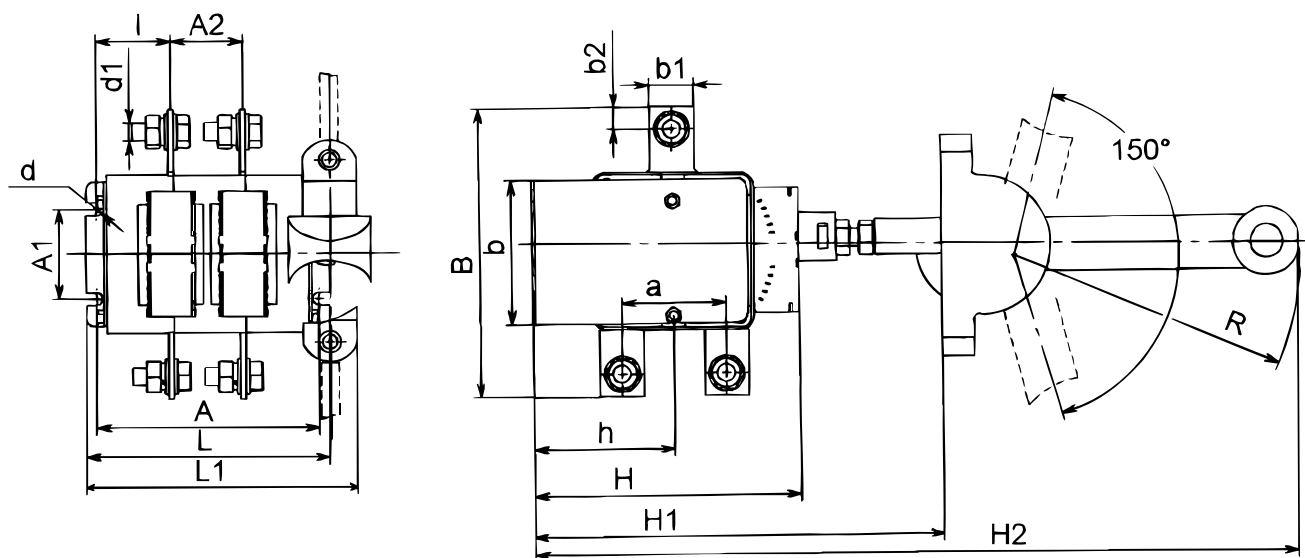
Выключатель-разъединитель на два направления двухполюсный с передней смещенной рукояткой
